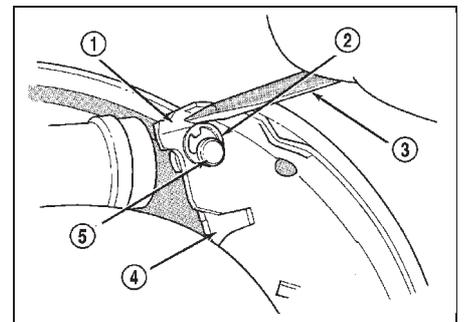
Установка стопорного кольца пальца рычага стояночного тормоза. 1 - тормозная колодка, 2 - стопорное кольцо, 3 - отвертка, 4 - рычаг стояночного тормоза, 5 - палец рычага стояночного тормоза.
